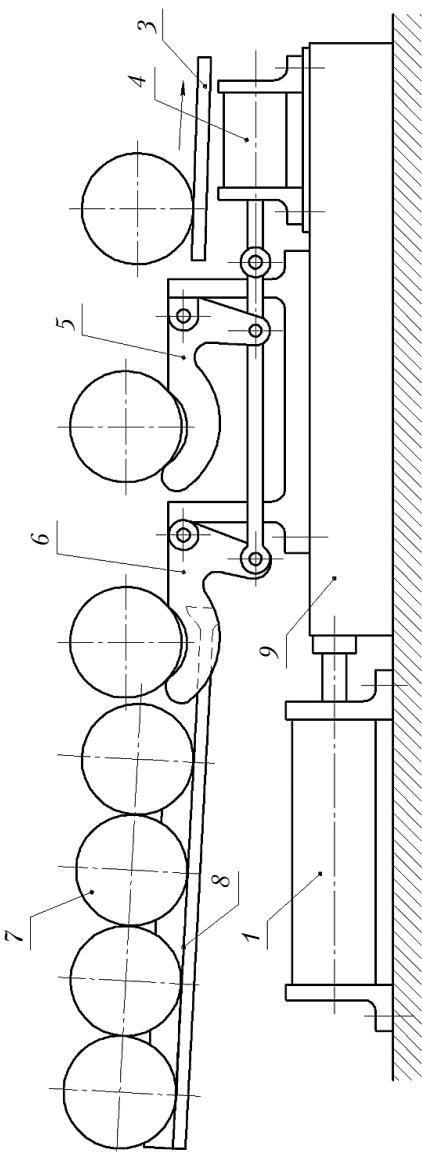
Схема автоматизированного устройства для установки зубчатых колес на центры швинговального станка и снятия с них
